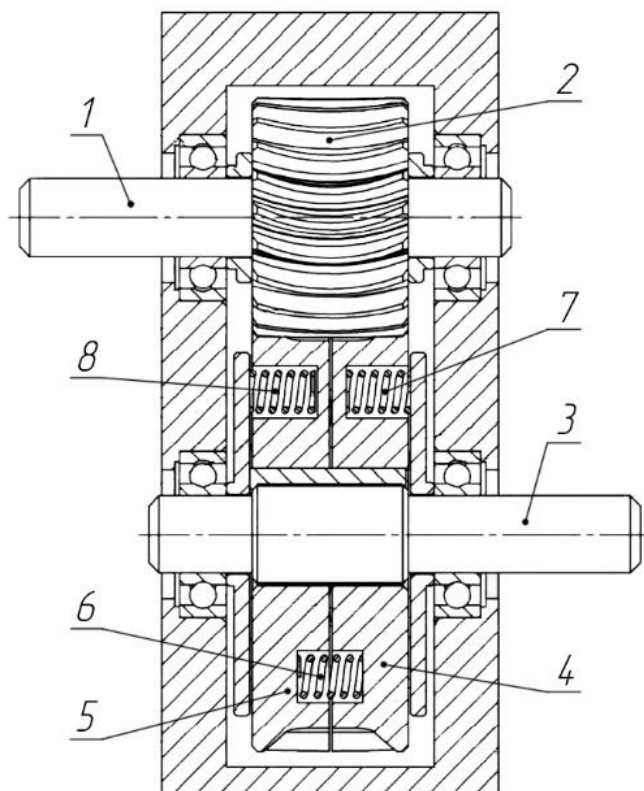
Адаптивная цилиндрическая передача с арочными зубьями [9]:
